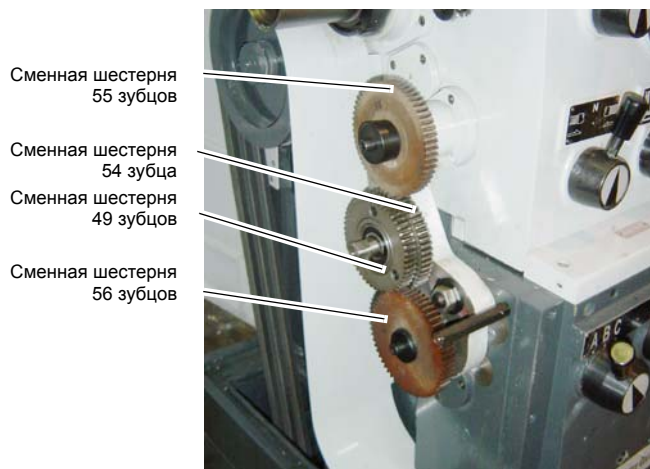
Расположение шестерен для метрической и дюймовой резьбы
